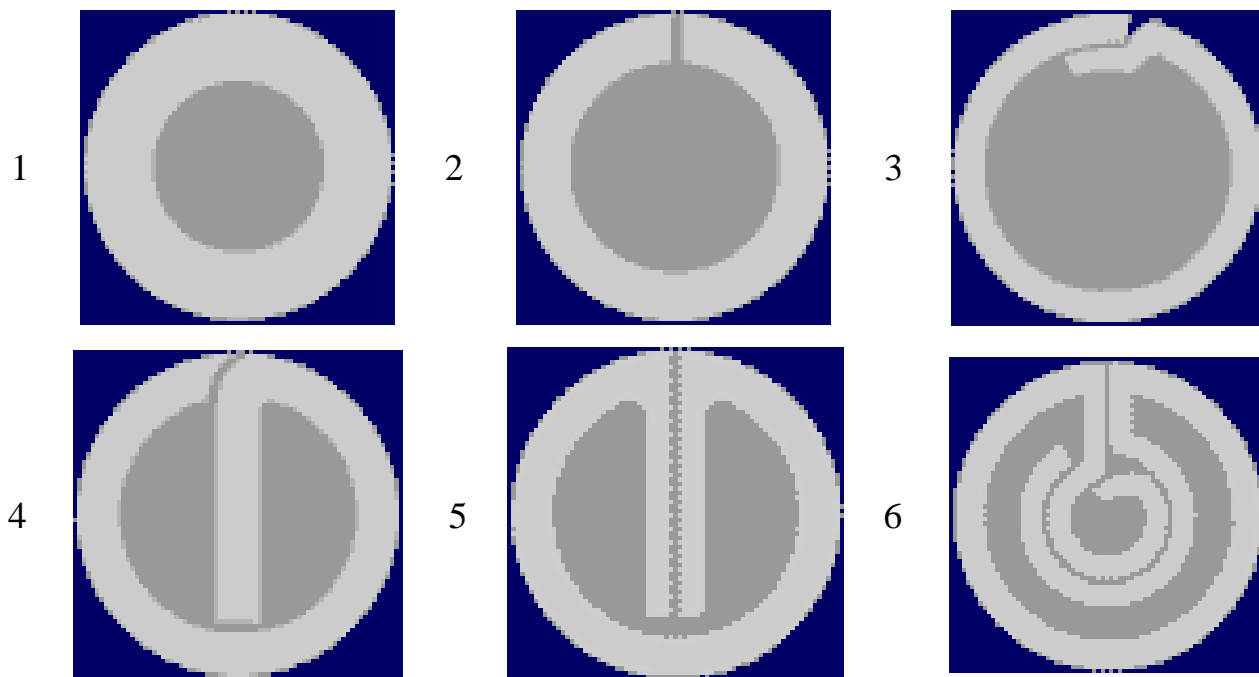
Найпоширеніші схеми конструкції замка ПД для наплавлення та наплення.
